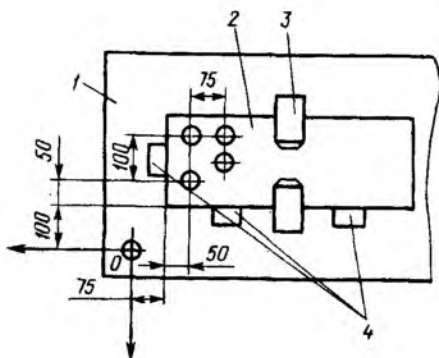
Базирование заготовки относительно нулевой точки станка:
